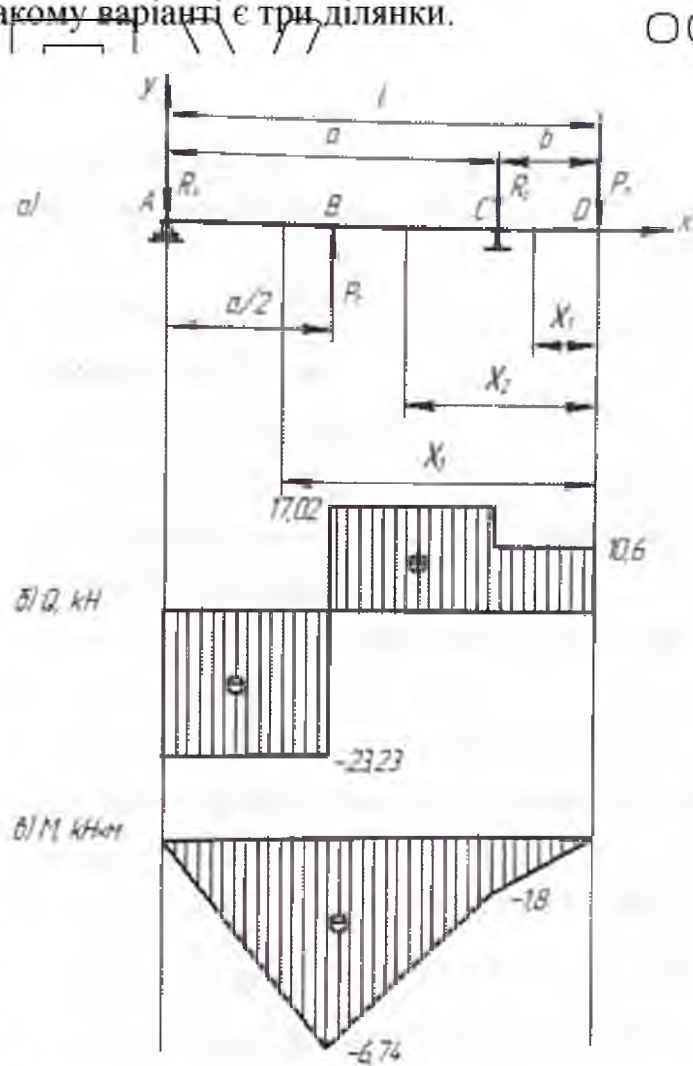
Розрахункова схема поперечної балки начіпки плуга
